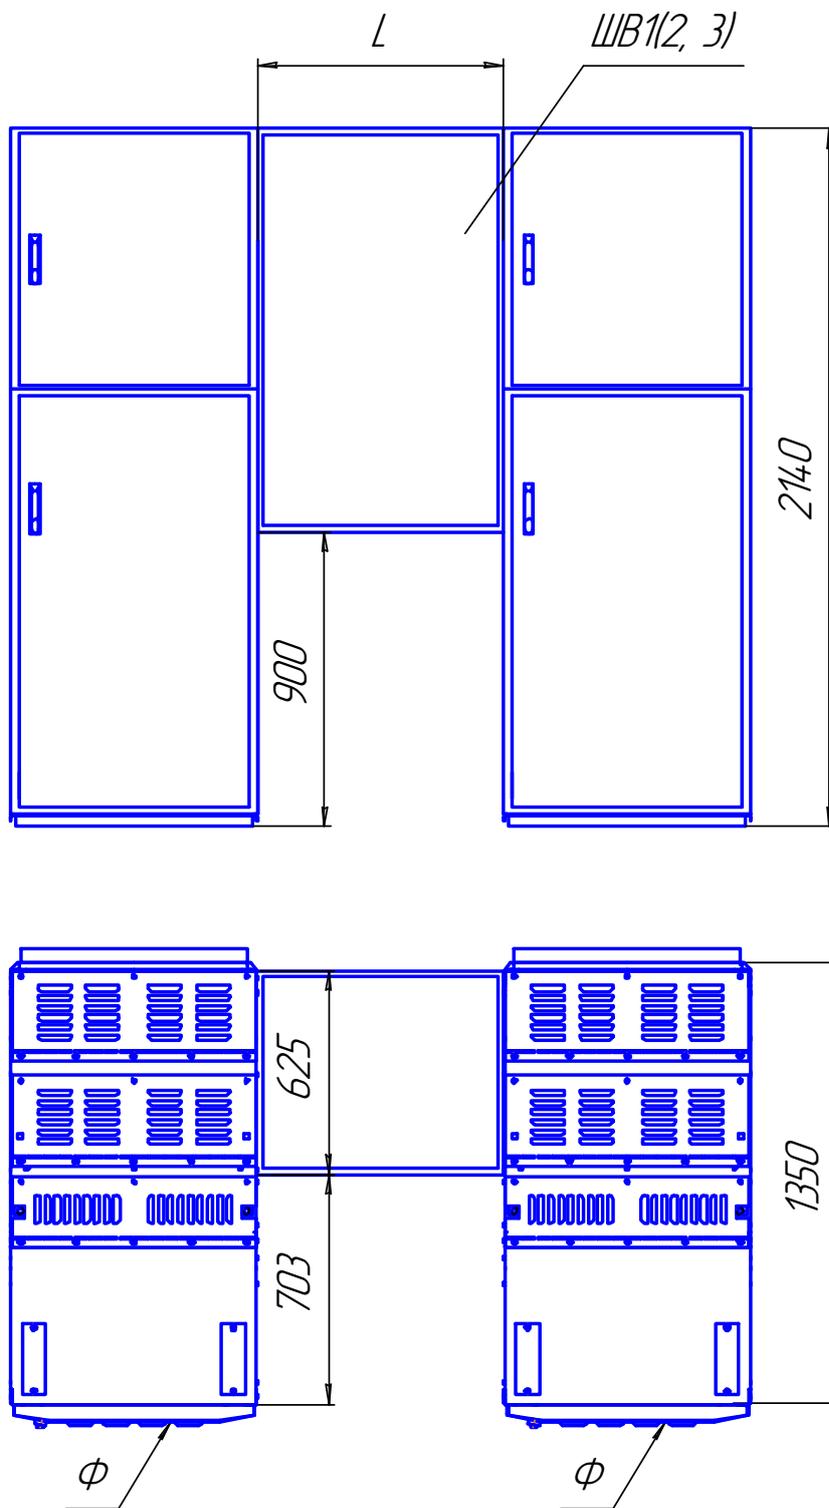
Габаритные, установочные и присоединительные размеры шинных вставок ШВ (сх.723, 1723)
